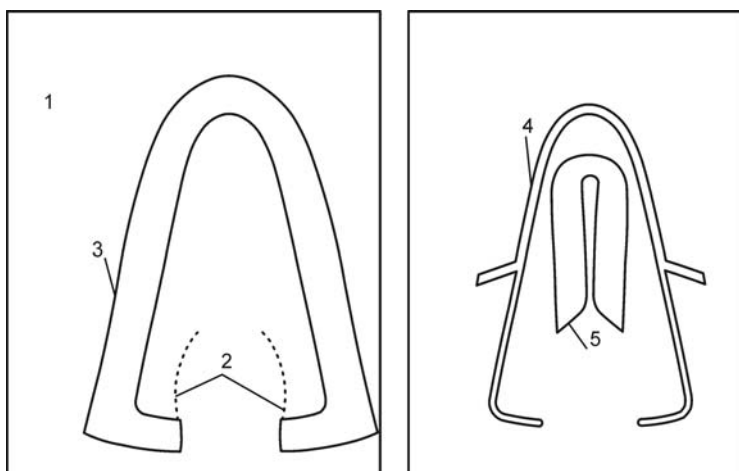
Пластины кассеты для сборки заготовки на полуавтомате
